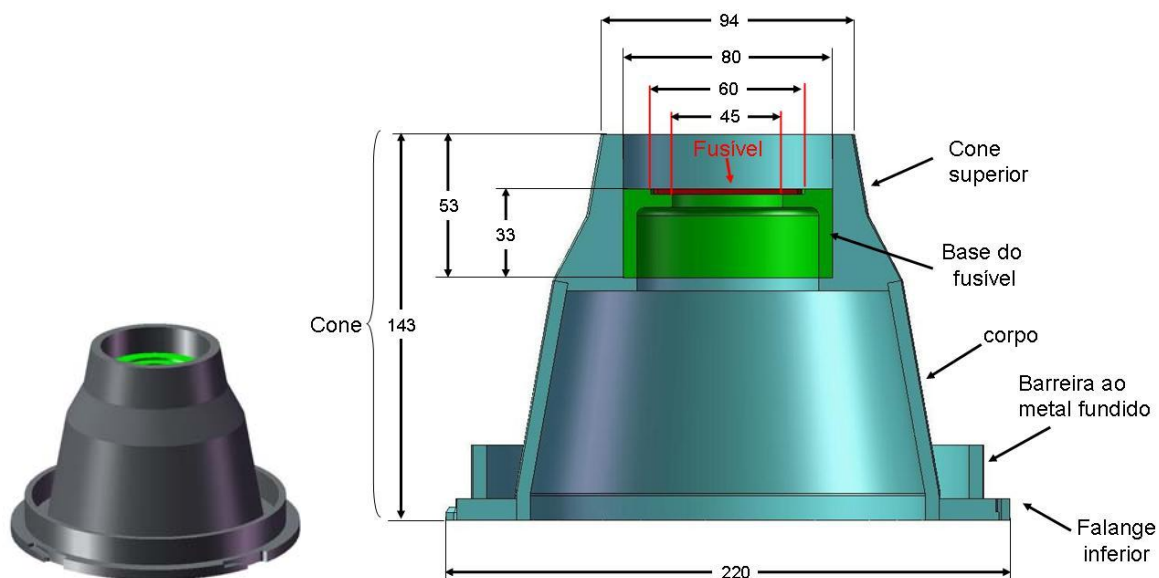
Falange do cadinho. Corte da flange do fusível com os dois elementos que a constituem: cone e base do fusível.
